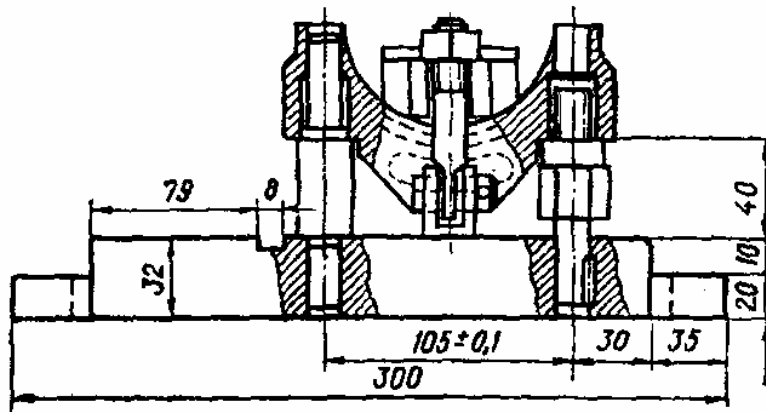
Пристрій для встановлення кришки шатуна під час фрезерування (шліфування) поверхонь рознімання
